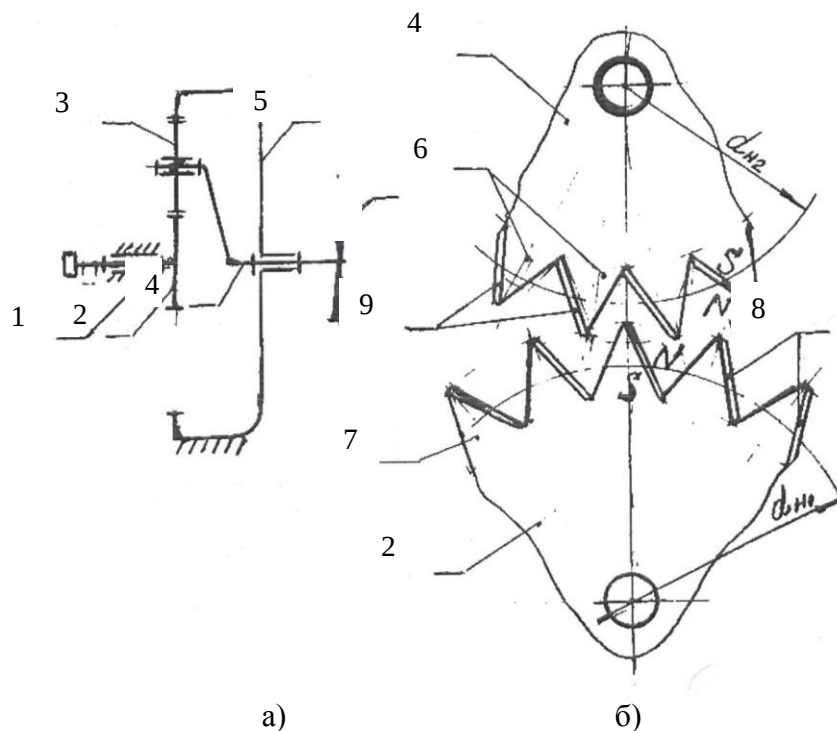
Планетарный редуктор с магнитными связями звеньев (а,б):
